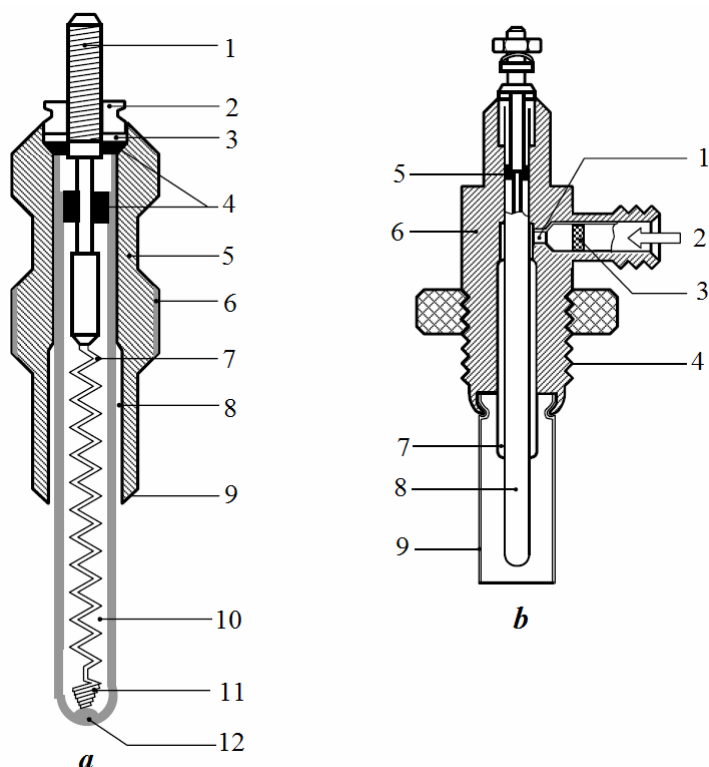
Bujii pentru preîncălzirea amestecului: a- bujie incandescentă: 1- conector electric; 2- piuliță; 3- șaibă izolatoare; 4- izolații electrice; 5- corp; 6- filet fixare; 7- înfășurare de control; 8- tub protecție; 9- scaun conic; 10- material izolant electric; 11- înfășurare încălzire; 12- vârf incandescent; b- bujie cu flacără: 1-orificiu dozare; 2- admisie combustibil; 3- filtru combustibil; 4- filet fixare; 5-garnitură; 6- corp bujie; 7- tub vaporizare; 8- corp incandescent; 9- manșon cu fante.
